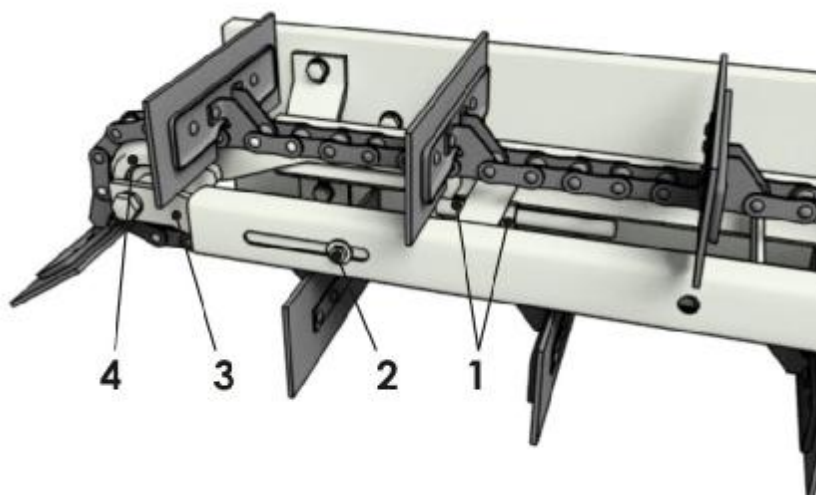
Регулировка натяжения скребковой цепи питателя
